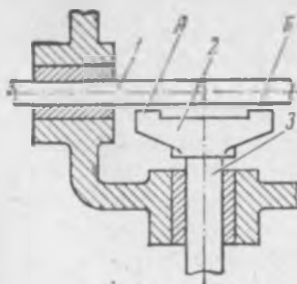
Приспособление для проверки перпендикулярности осей конической пары редукторов.
